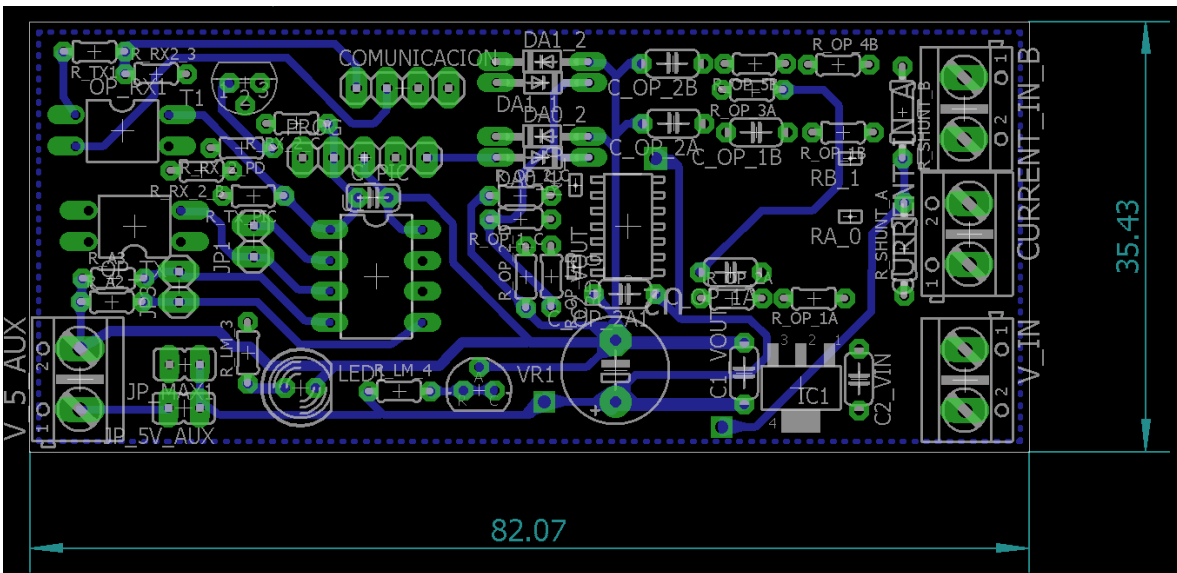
PCB módulo de medición – Bottom Layer.
